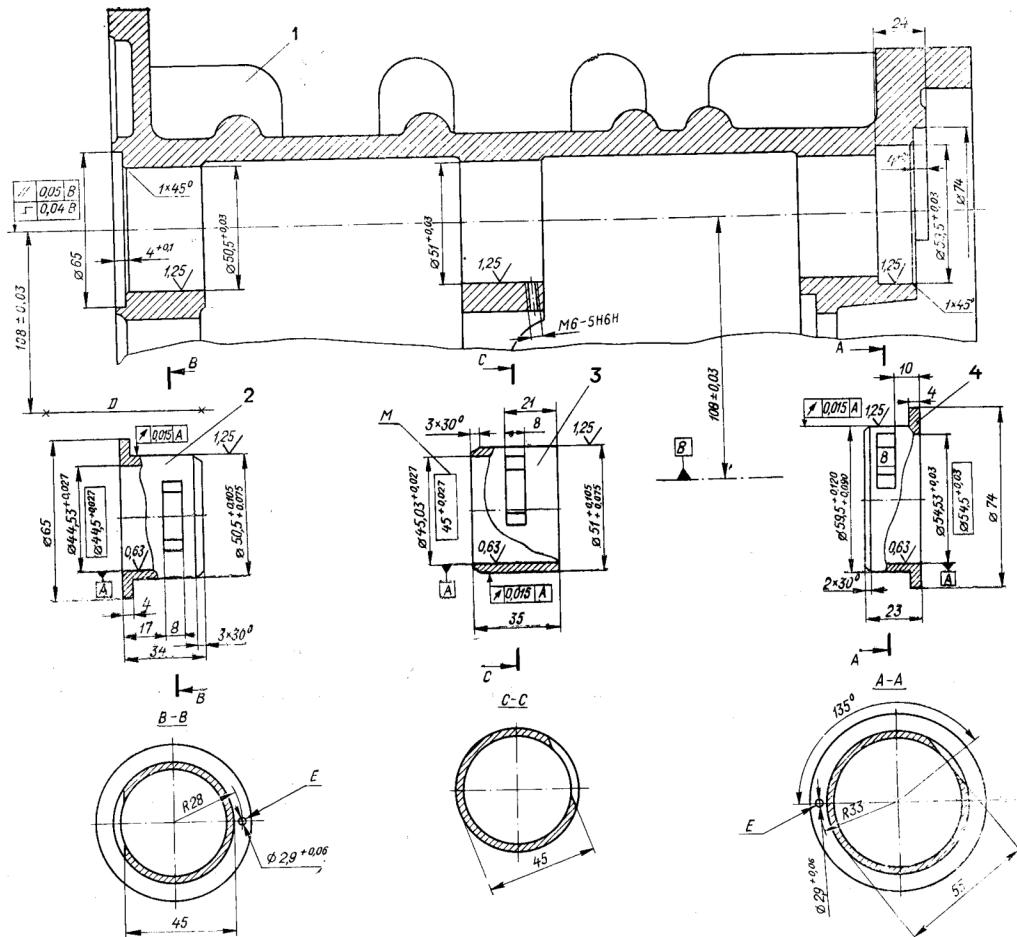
Расточка картера двигателя под ремонтные подшипники распределительного вала:
